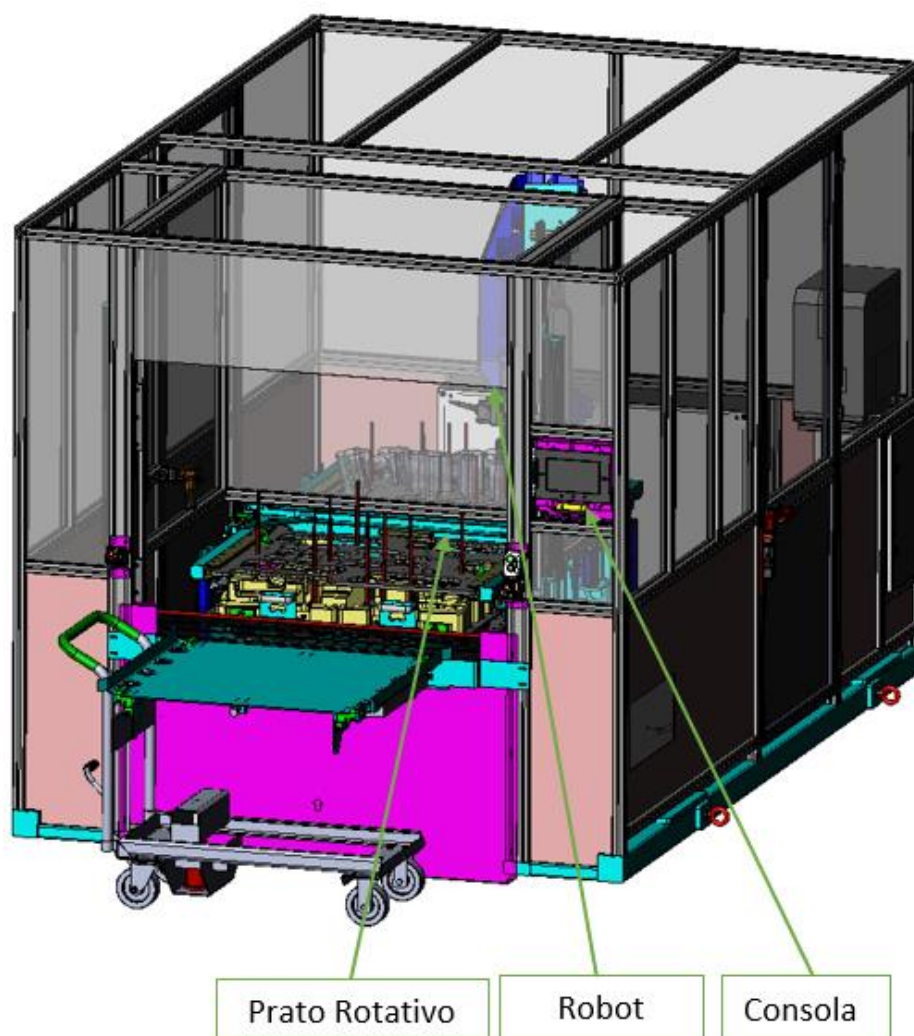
Célula de soldadura com 1 robô [documentação interna].
